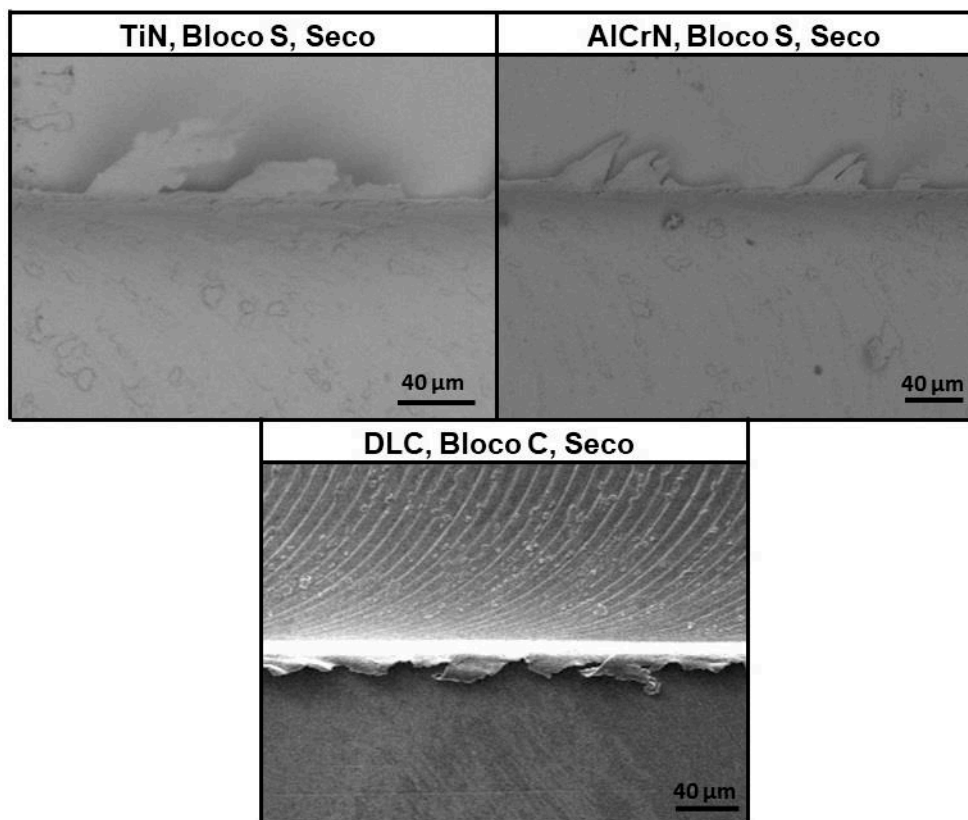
Rebarbas semelhantes as rebarbas do tipo primária.
